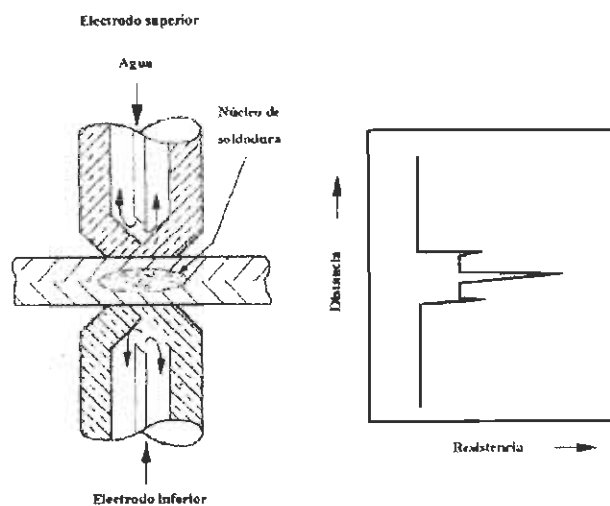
Esquema representativo de la soldadura por puntos ^[14]
